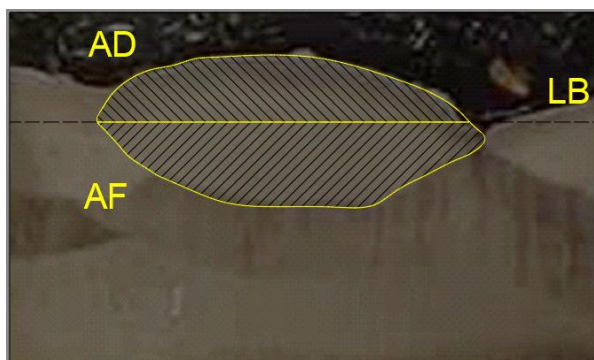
Região de medição do Perfil Geométrico do cordão de solda
